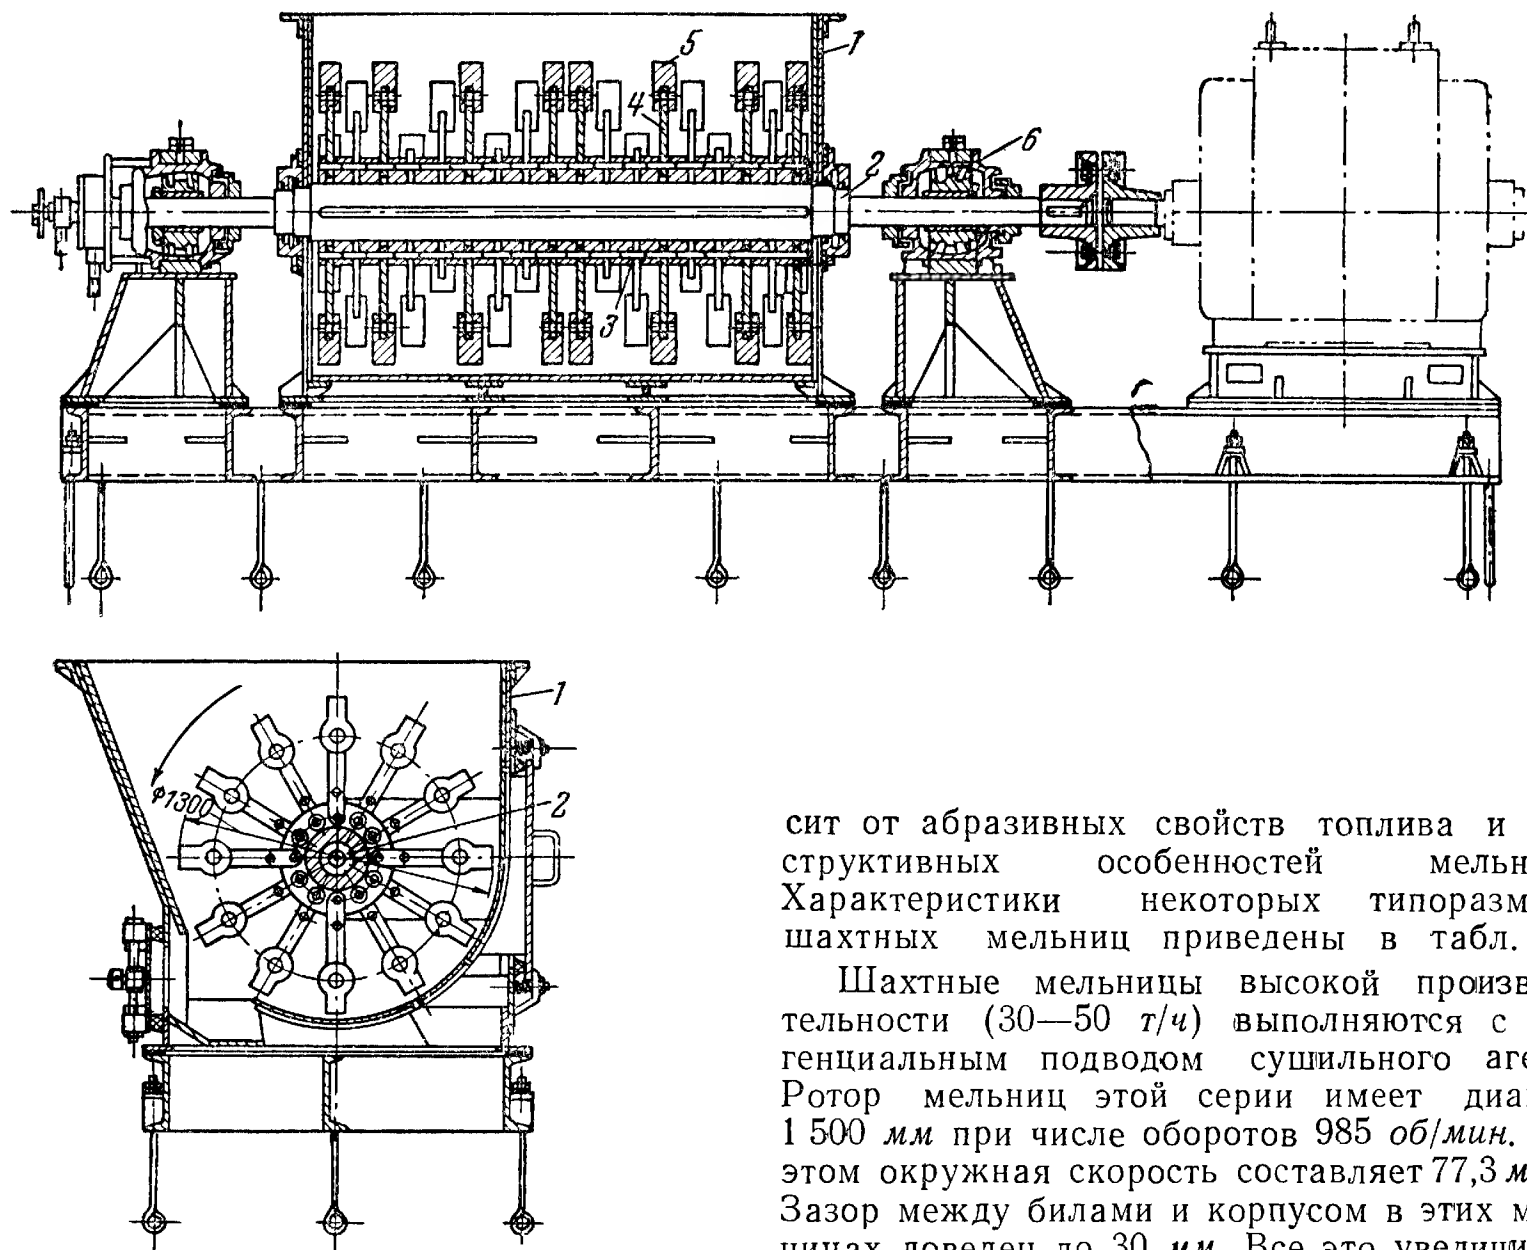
Конструкция ротора и корпуса шахтной мельницы.
